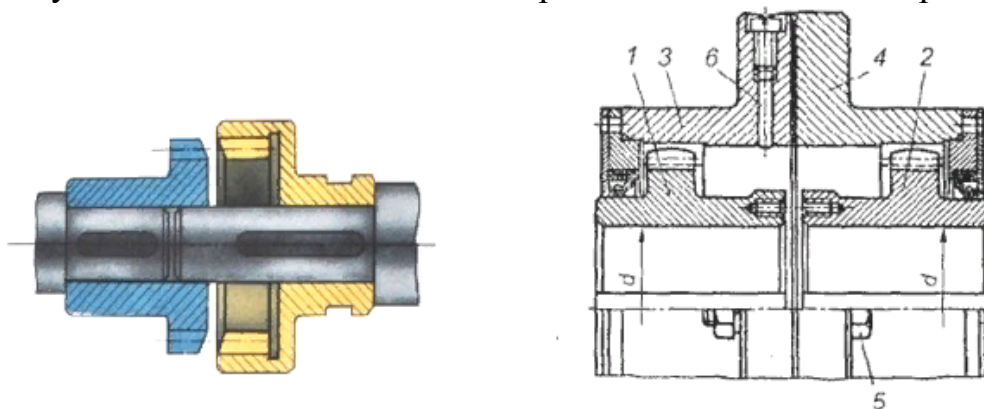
Конструкция зубчатой муфты: 1, 2 – полумуфты; 3, 4 – барабаны; 5 – болт; 6 – отверстие
